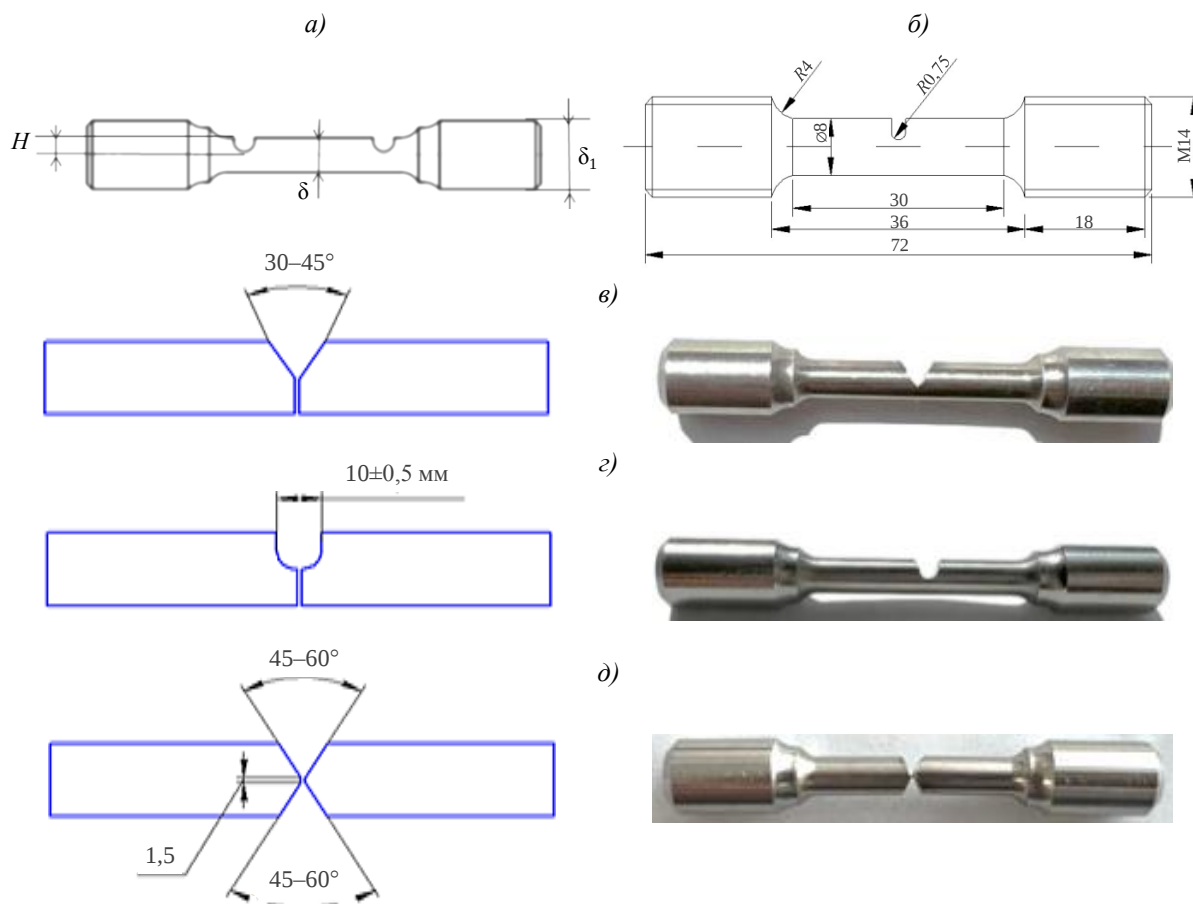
Схемы выборки: а – эскиз образца (H – размер выборки; δ – ширина рабочей части заготовки; δ_1 – высота головки заготовки); б – эскиз заготовки образца с разделкой применительно к технологии ремонта; в–д – заготовки с V-образной, U-образной и двухсторонней разделкой
